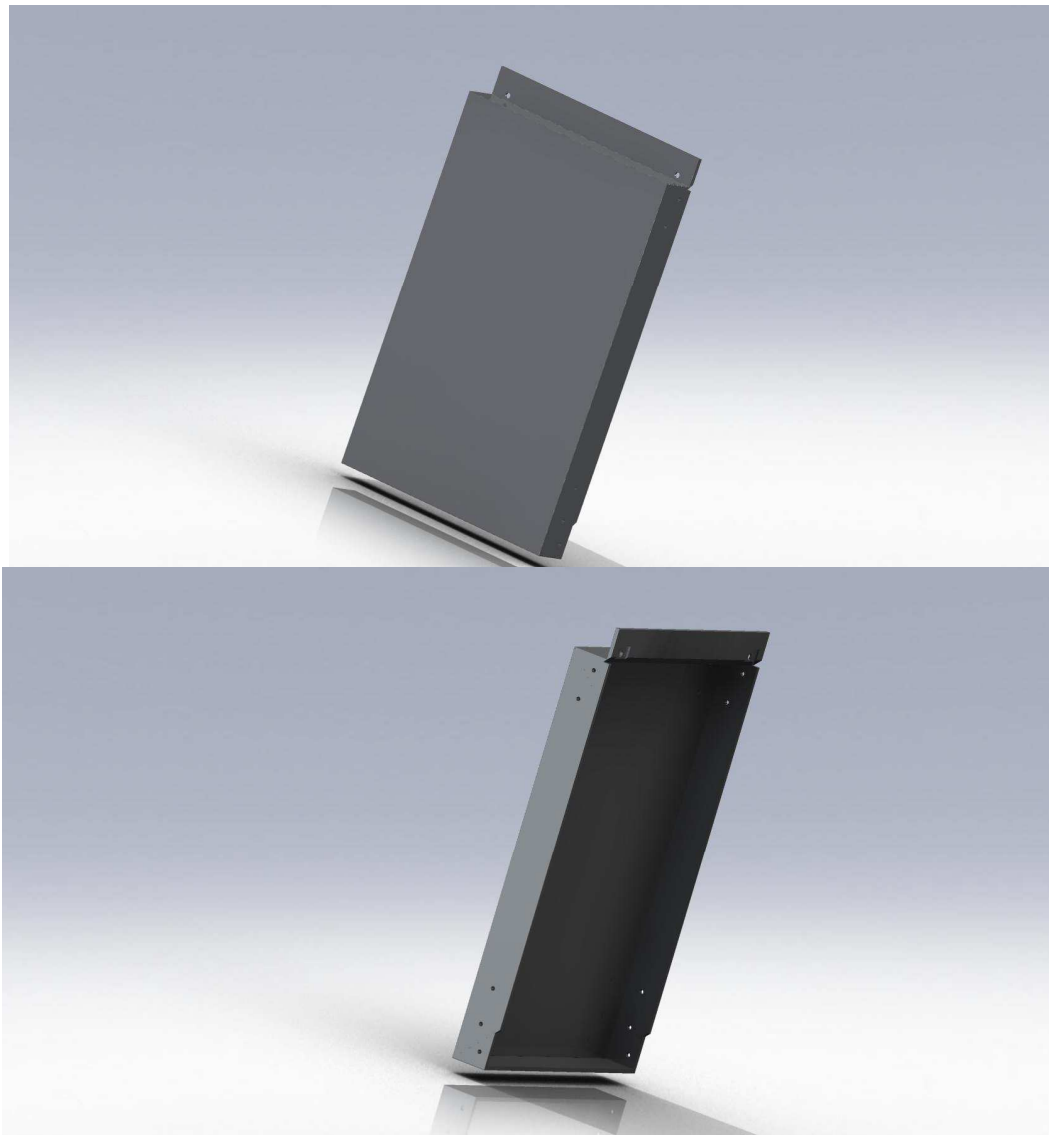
Detalj postavljanja ploče na podkonstrukciju-bočni pogled
